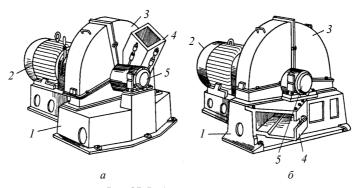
Рубительные машины: a-c наклонным расположением загрузочного люка; $\delta-c$ горизонтальным расположением загрузочного люка; $I-\phi$ ундаментная рама; 2- электродвигатель; 3- кожух ножевого диска; 4- загрузочный люк; 5- корпус главного подшипника
